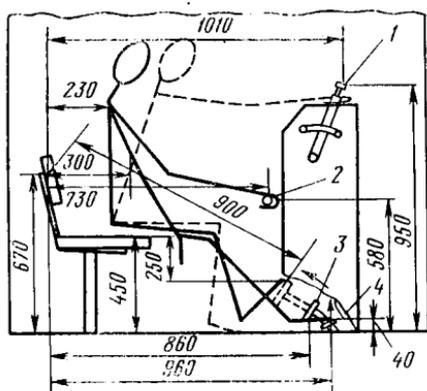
Схема рабочего места водителя-моториста агрегата 3ЦА-400А:
